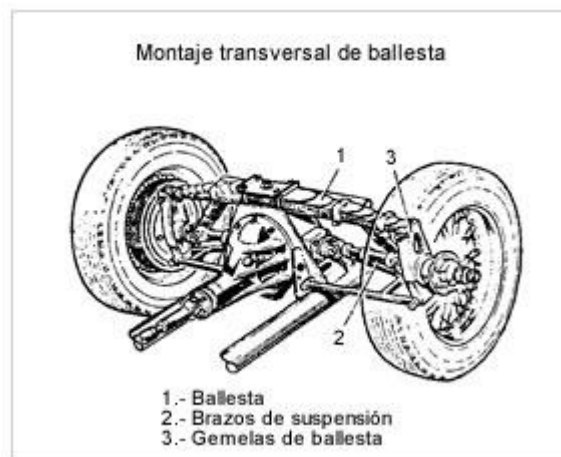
BALLESTA CON MONTAJE TRANSVERSAL.
